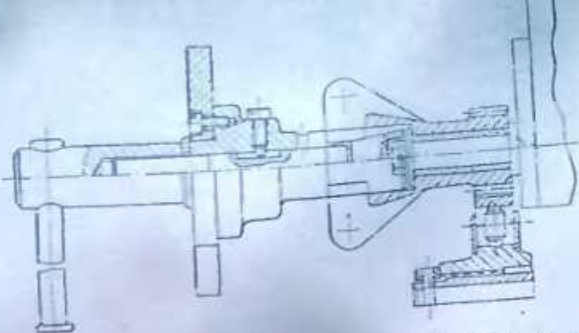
Приспособление для проверки зазора в зацеплении шестерни-водила регулятора с упругой шестерней топливного насоса
